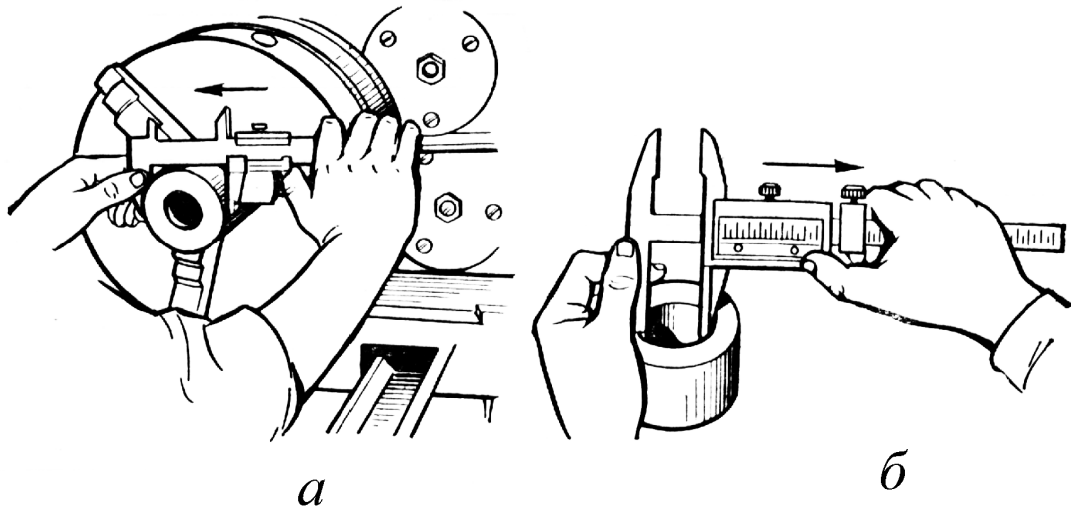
Измерение штангенциркулем наружных (а) и внутренних (б) размеров закрепленной детали
